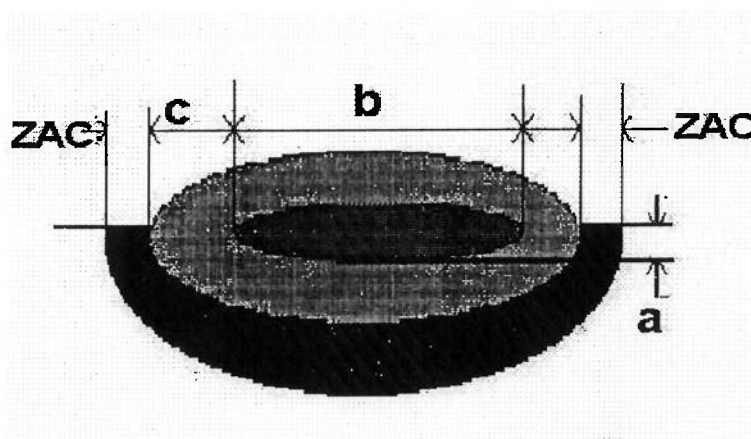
Dimensões principais que podem ser observadas em cordão de solda através da microscopia óptica. (Adaptado da referência 56)
